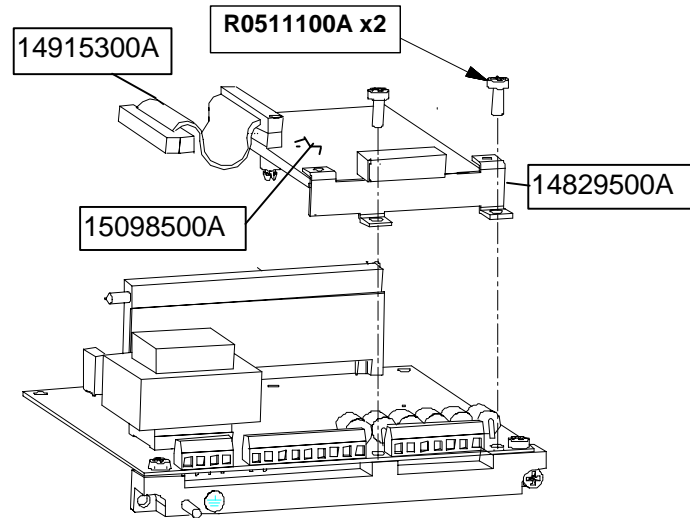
Instalación de la PCB Allen-Bradley en el gabinete de montaje en panel
